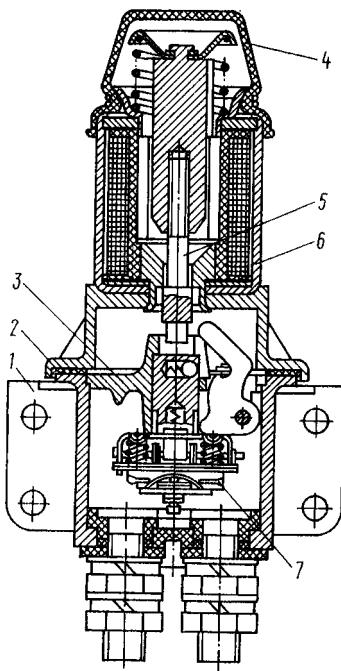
Выключатель тока типа ВК-860-В: 1 - корпус; 2 - прокладка уплотнительная; 3 - плита опорная; 4 - устройство ручного включения с защитным чехлом; 5 - шток; 6 - электромагнит; 7 - система контактная
